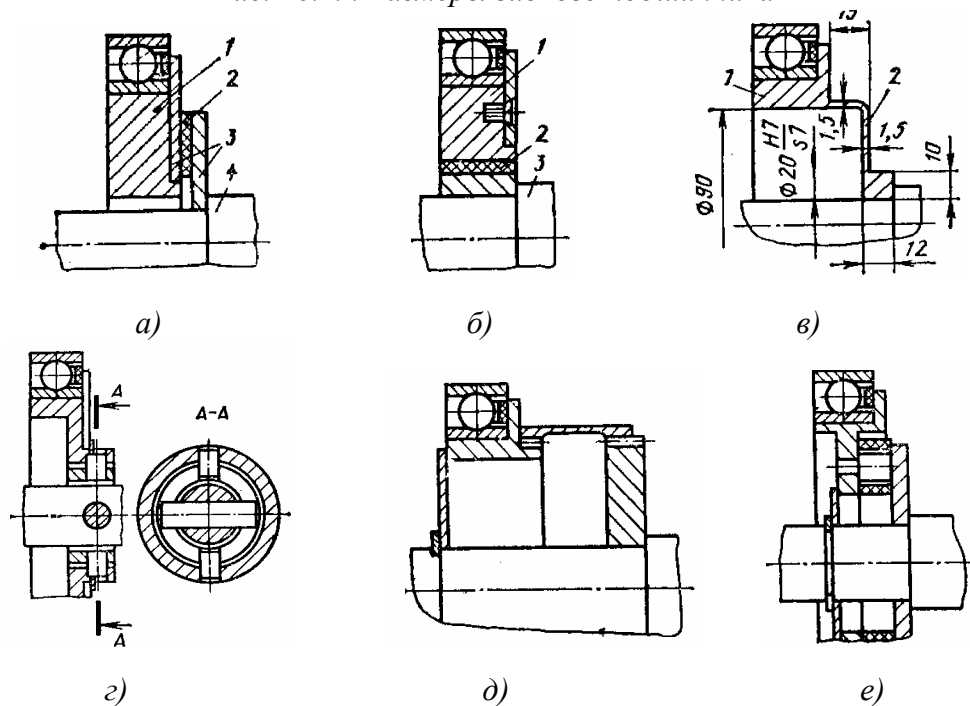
Варианты конструкции соединения кулачка с быстроходным валом редуктора
